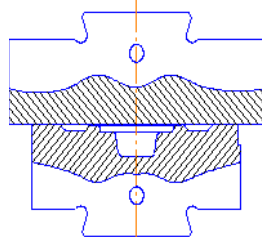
Штамп з універсальним плоским верхнім бойком для виготовлення деталей з тонкими фланцями
